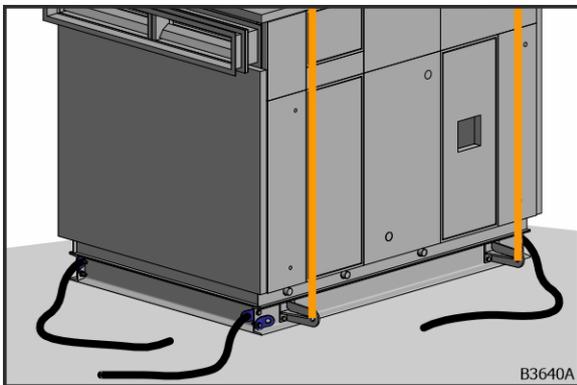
élingage de la centrale sur châssis DIN au niveau des équerres de levage
